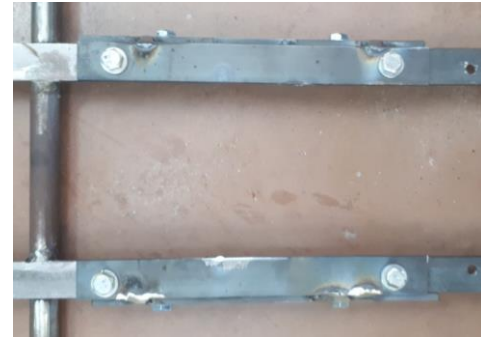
Barres i perfils soldats 1. Font: Elaboració pròpia
